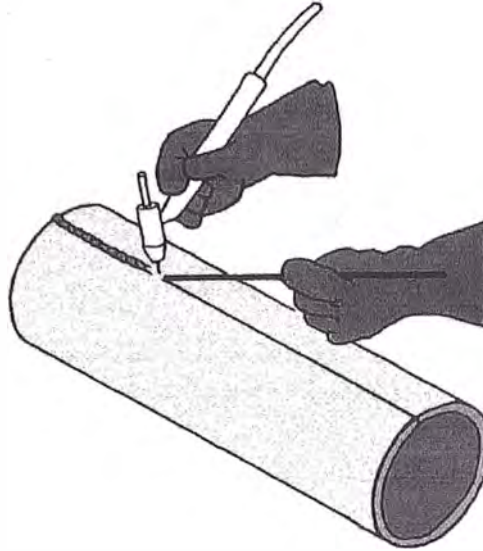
Disposición para soldadura de arco de tungsteno protegido por gas (Fuente: Manual de Soldadura Infra)
